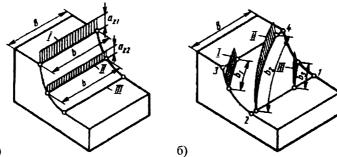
Параметры сечения среза при обработке цилиндрической фрезой с прямыми (а) и винтовыми (б) зубьями
